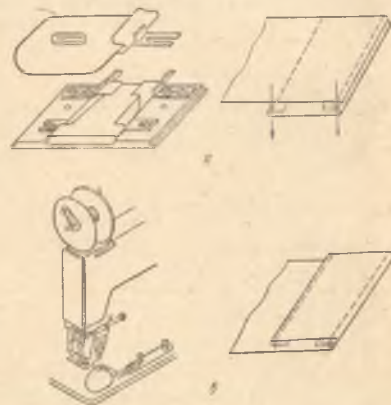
Приспособления для подгибания срезов деталей и их соединения
